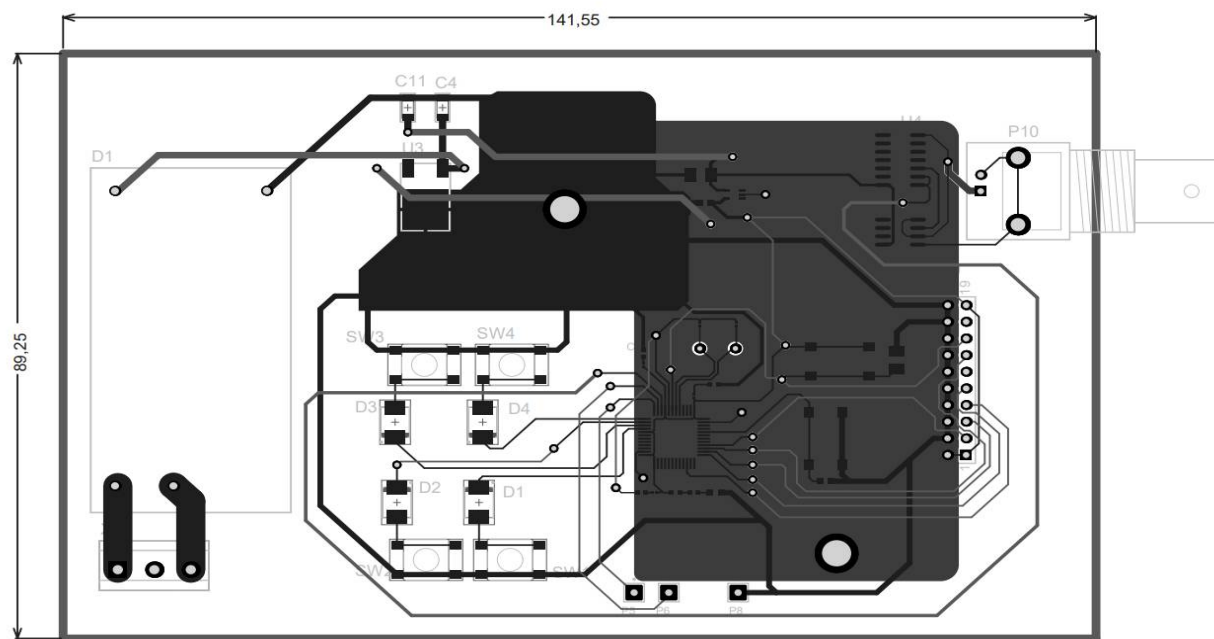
Сборочный чертеж печатной платы, проектируемой в AltiumDesigner
